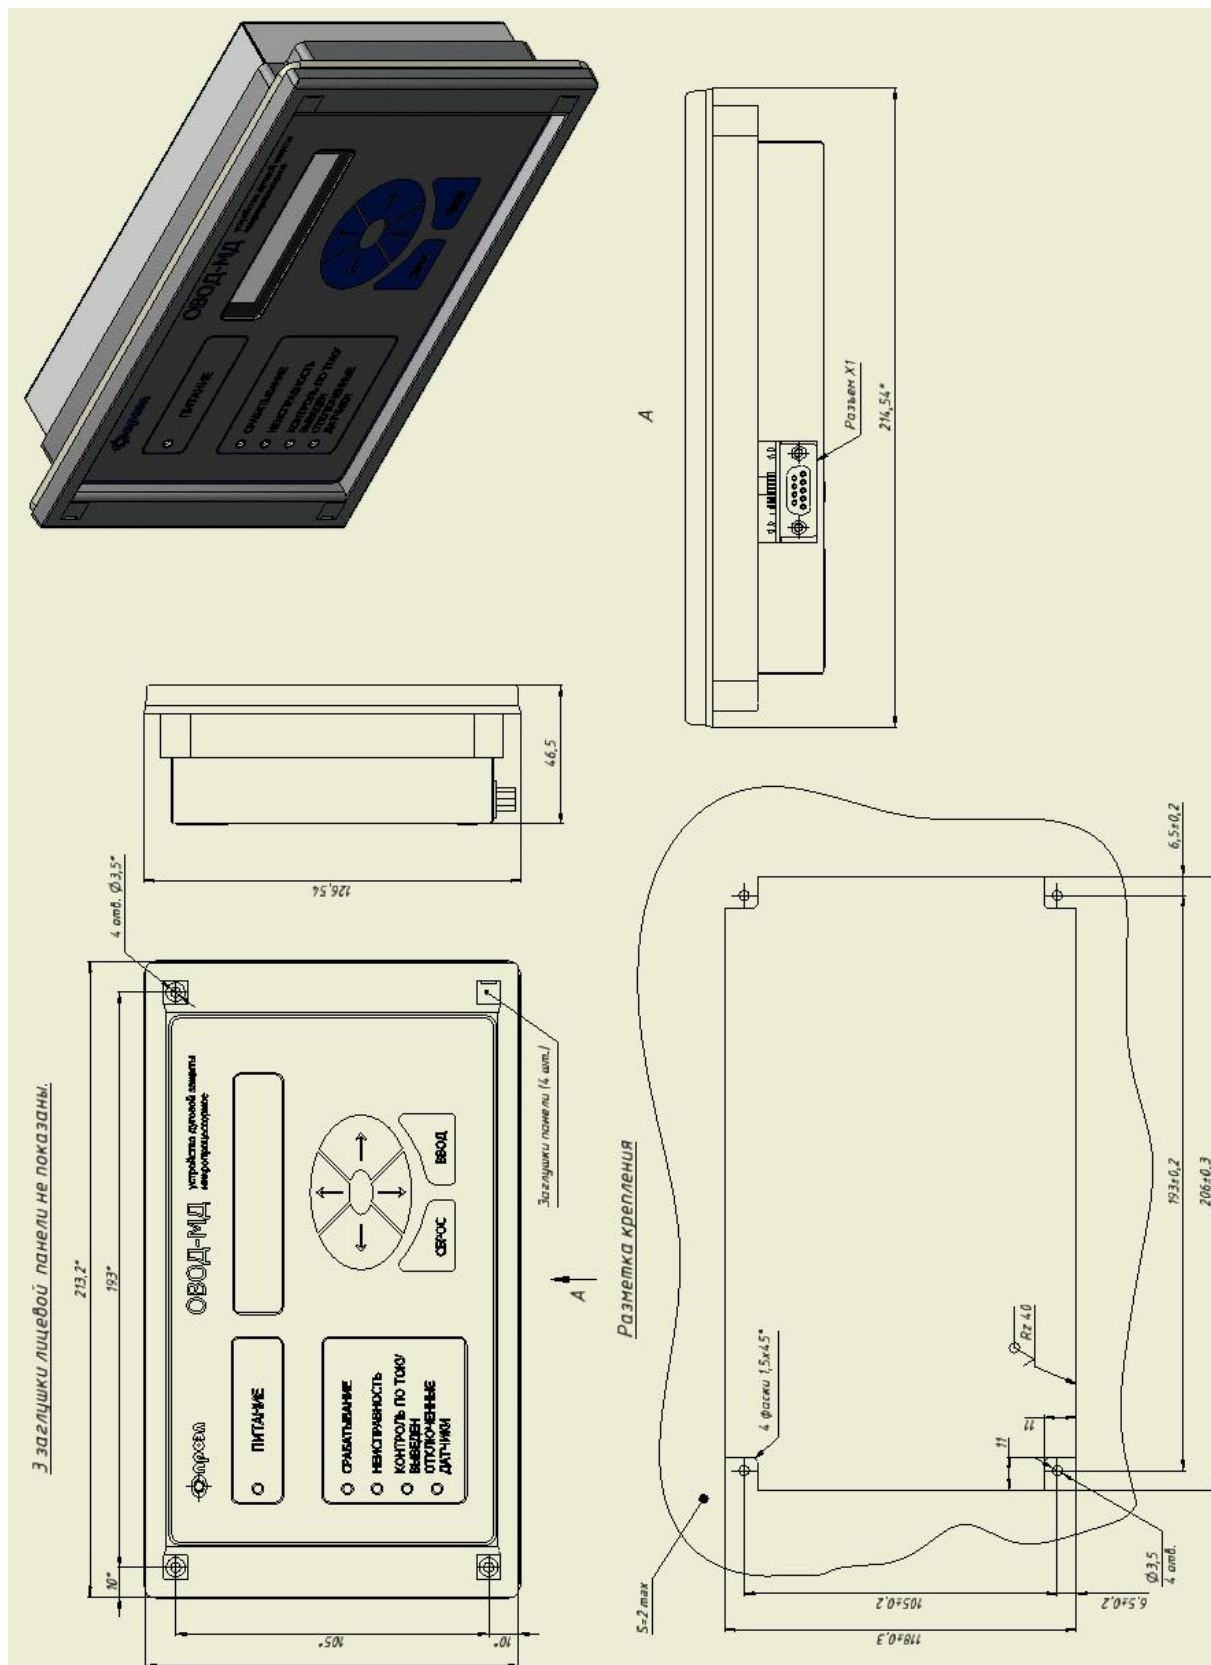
Габаритные размеры блока управления и размеры посадочного места
